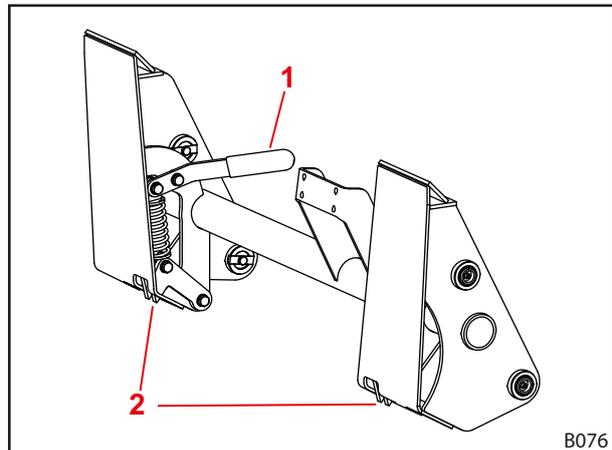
Werkzeugverriegelung am Skid-Steer-Wechselrahmen
